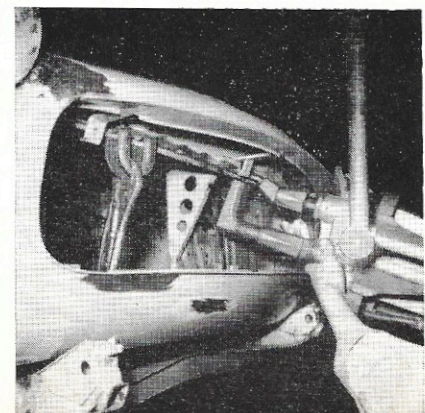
Mise en place du revêtement complet après soudage des divers éléments à la soudure oxyacétylénique (flèches).
